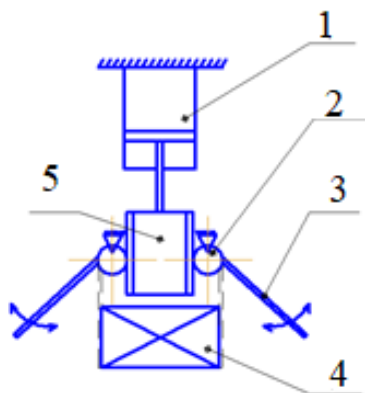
Схема механічного захоплювального пристрою рейково-важільного типу з коливальним рухом стулок: 1- пневмоциліндр двосторонньої дії; 2- циліндричні зубчаті колеса; 3 – стулки; 4- упаковка; 5 – зубчаста рейка
